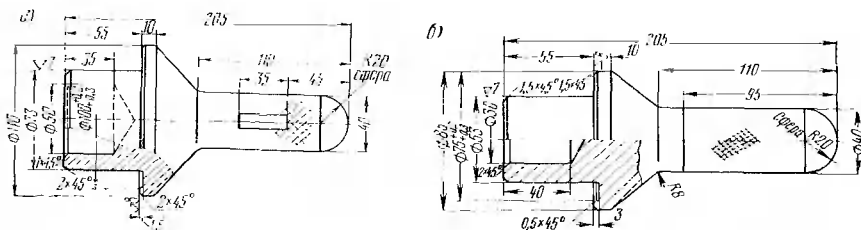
Оправки для напрессовки подшипников на шейки чашек дифференциала заднего моста:
